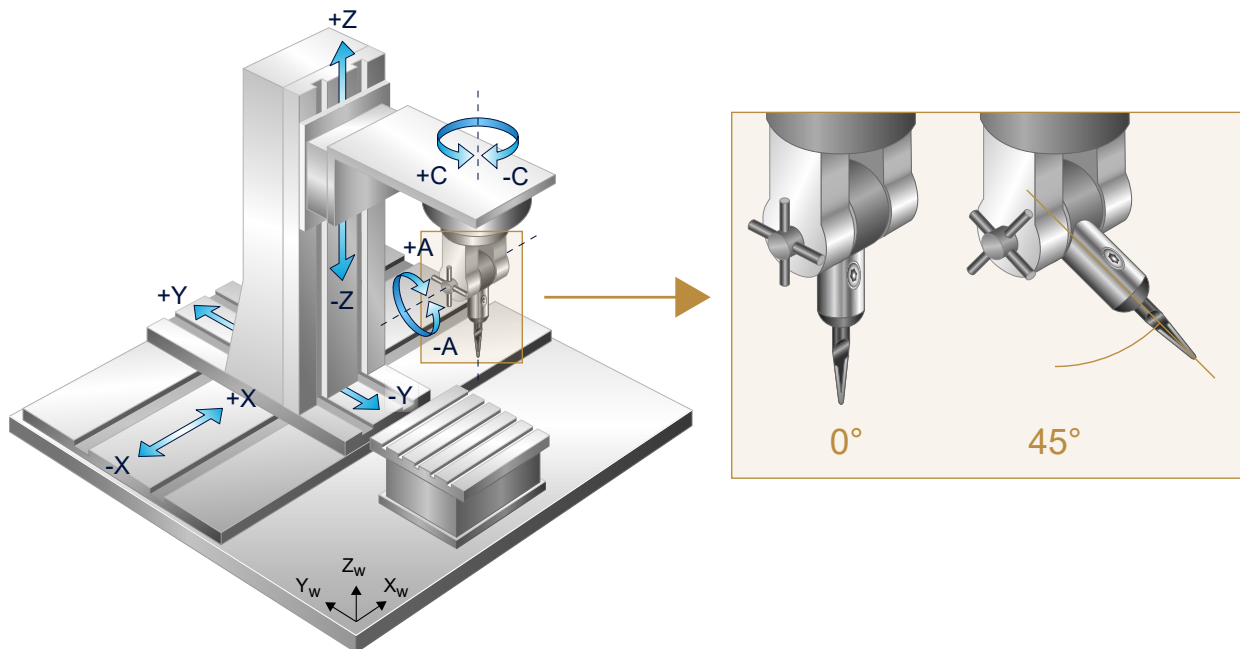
5-achsige Kinematik (Schneidwerkzeug mit manueller Hilfsachse A)
